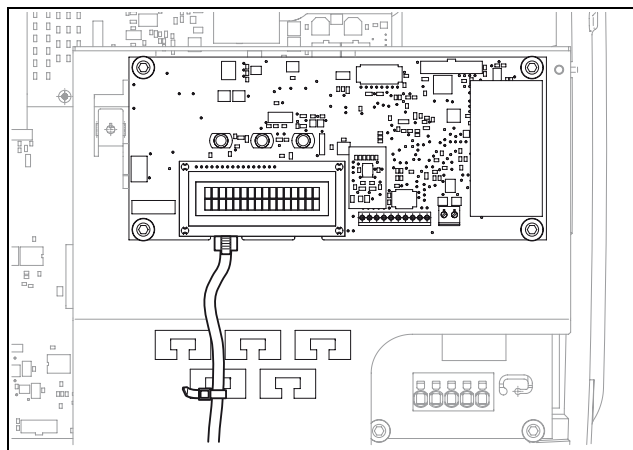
fissaggio dei cavi alla lamiera di protezione (solo PIKO 8.3/10.1)
